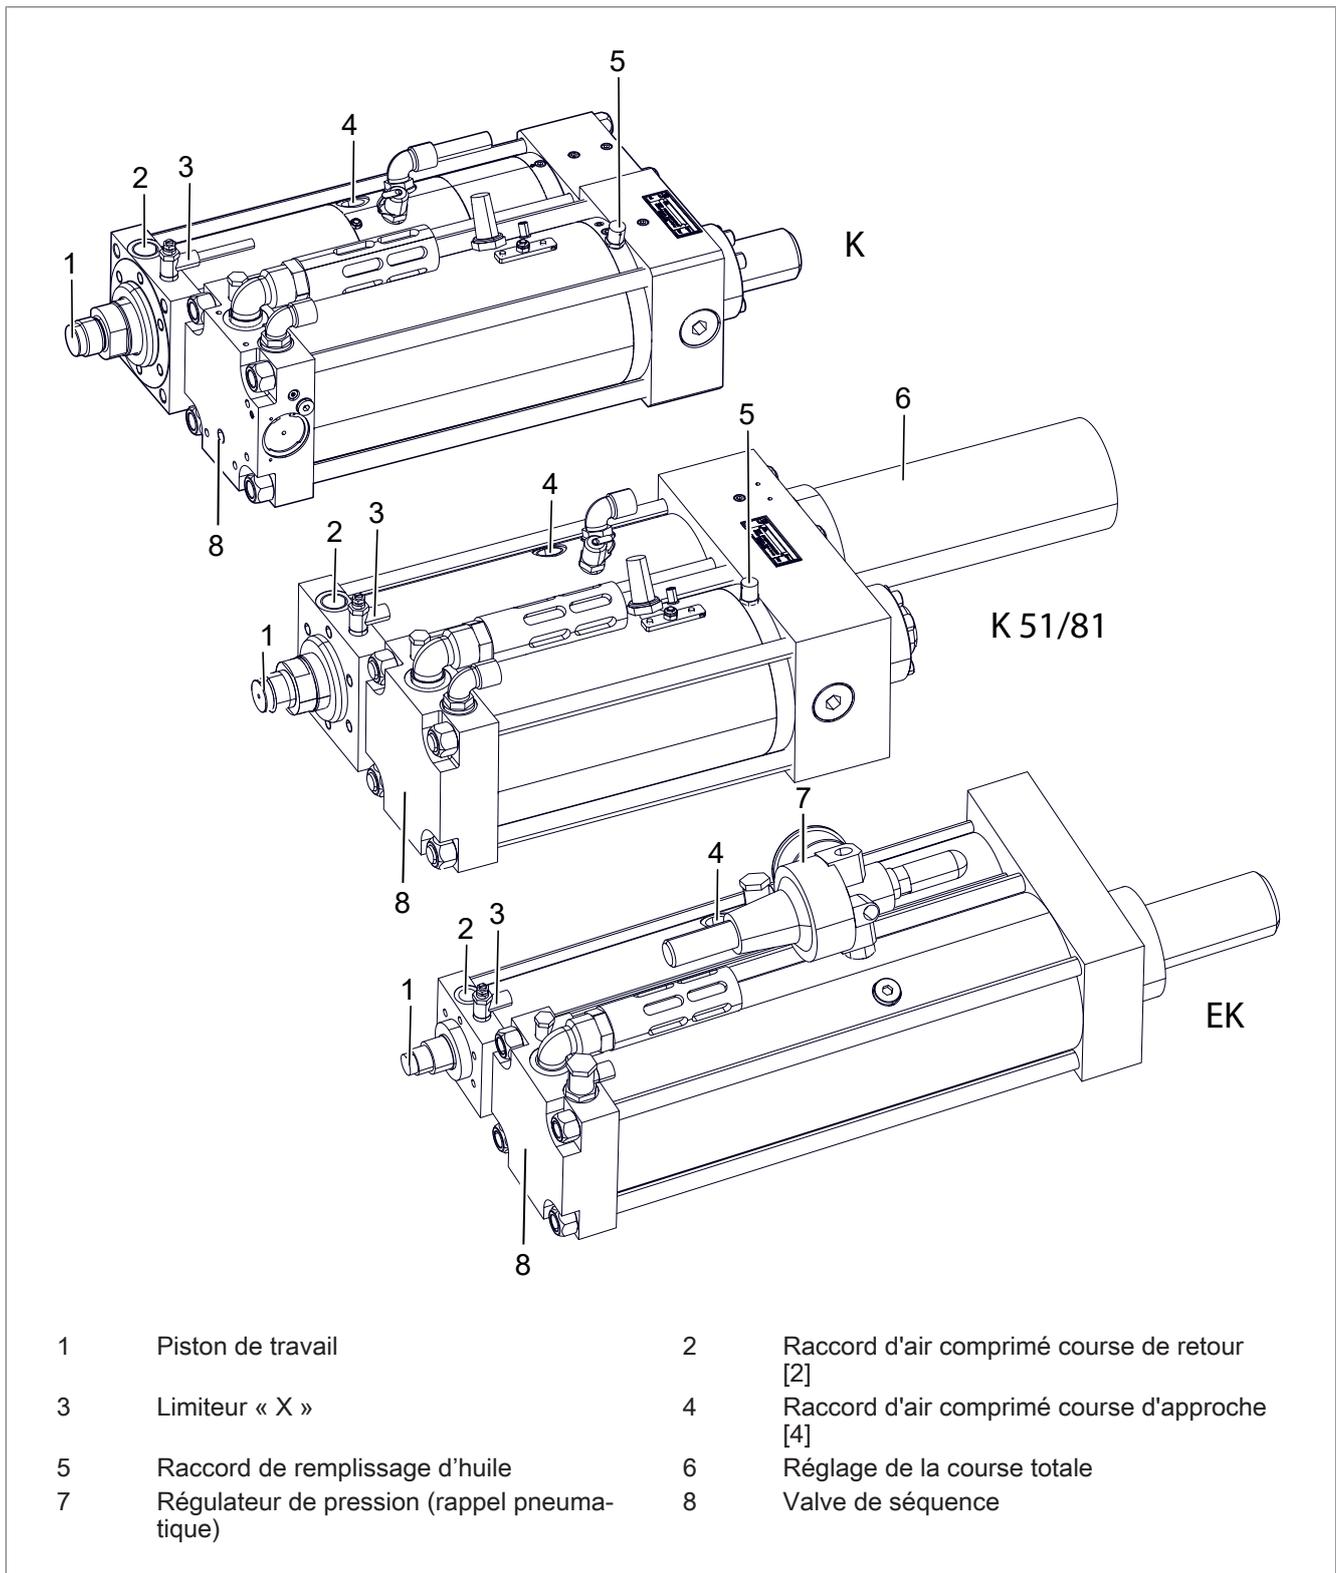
Vue d'ensemble du modèle K, EK, K, version 51/81
